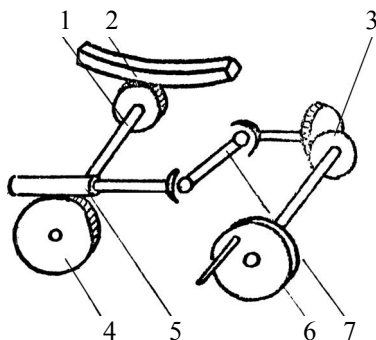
Схема секторного механізму із зовнішнім зчепленням корінної шестерні:
